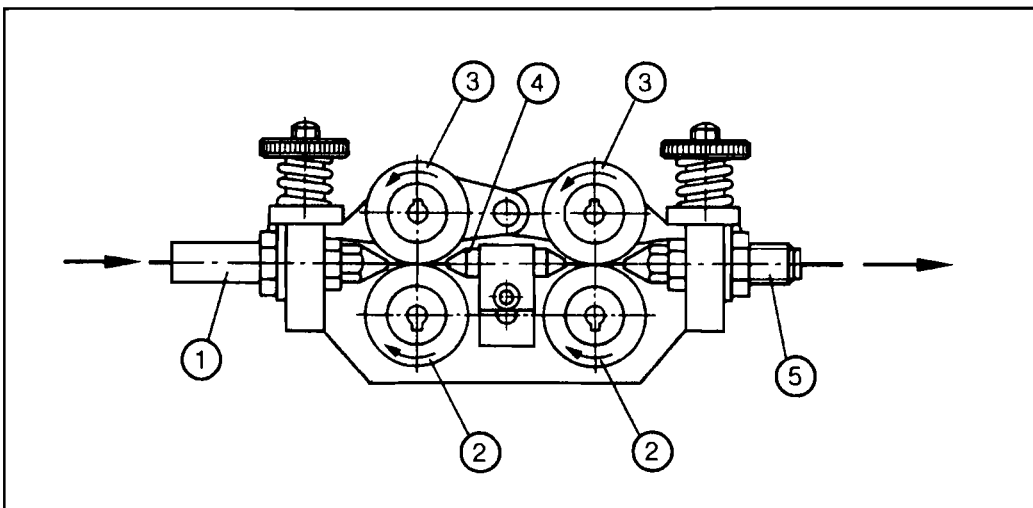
ALIMENTADOR DE ALAMBRE DE CUATRO RODILLOS
